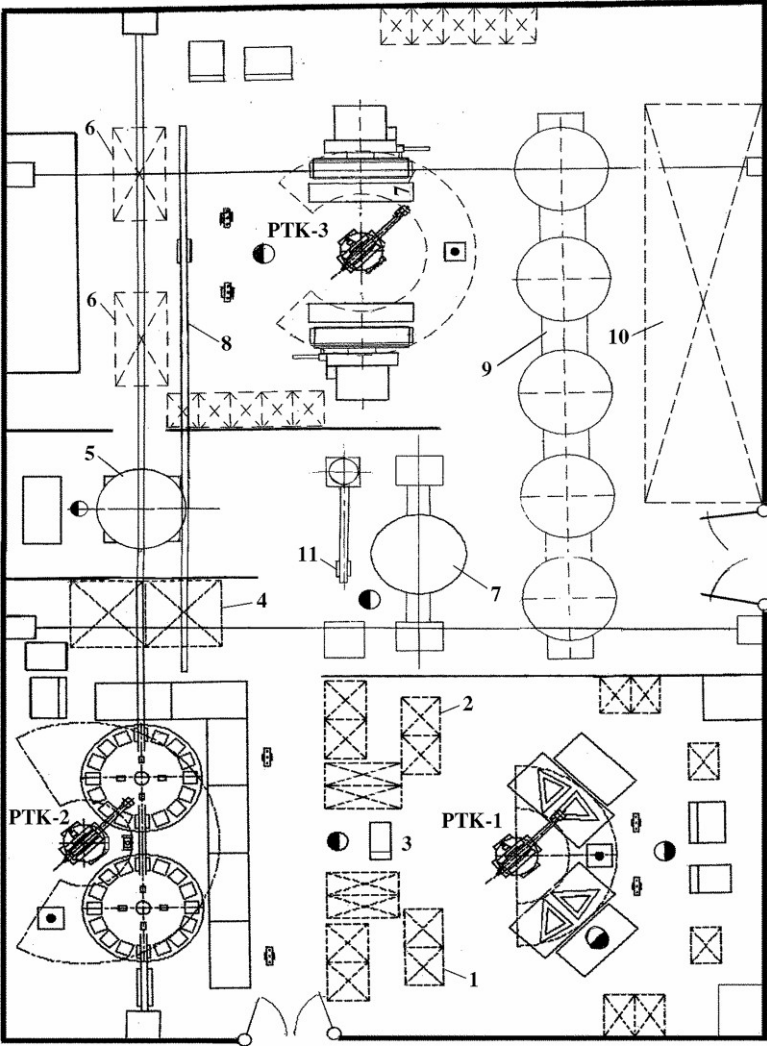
Схема участка роботизированной сварки барабана
